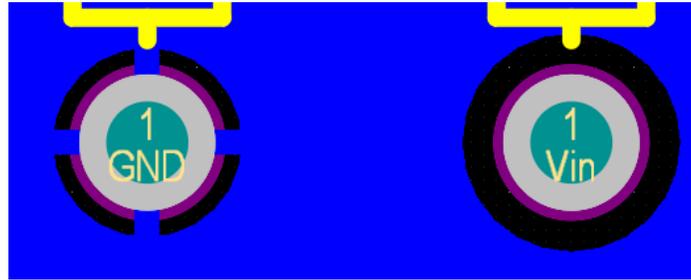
Detalle del plano a tierra en las conexiones que van a GND.
